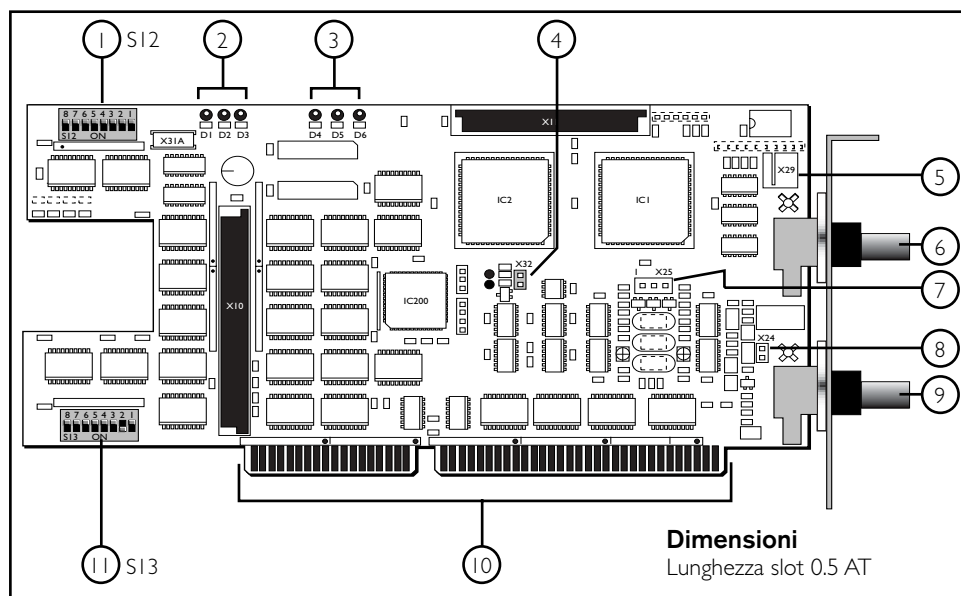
LBB 3511/00 PC Card per sistemi Multi-CCU
